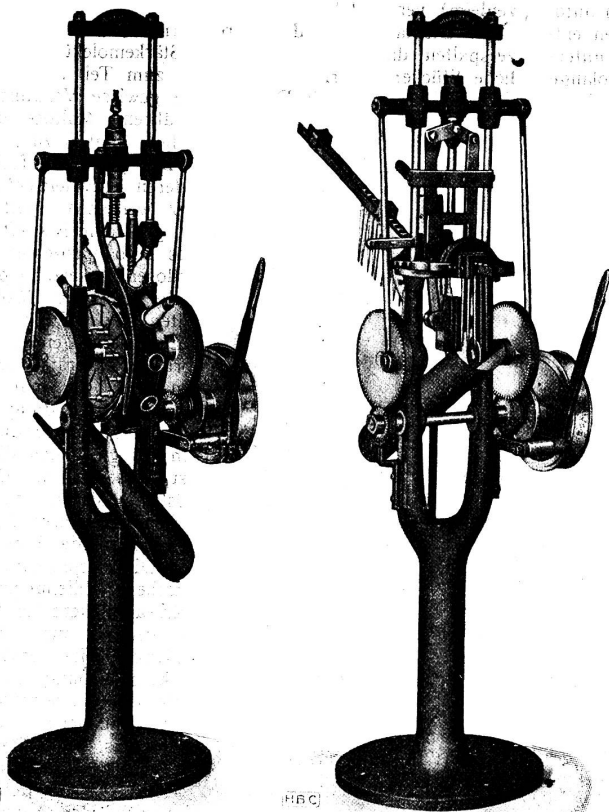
Bobinen-Aufsteckmaschine. Fig. 7. Hülsen-Abziehmaschine.
